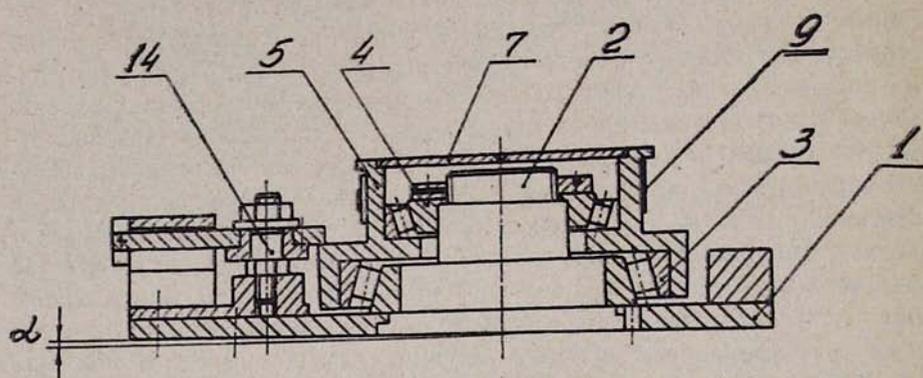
Приспособление для получения корня стружки при фрезеровании.
